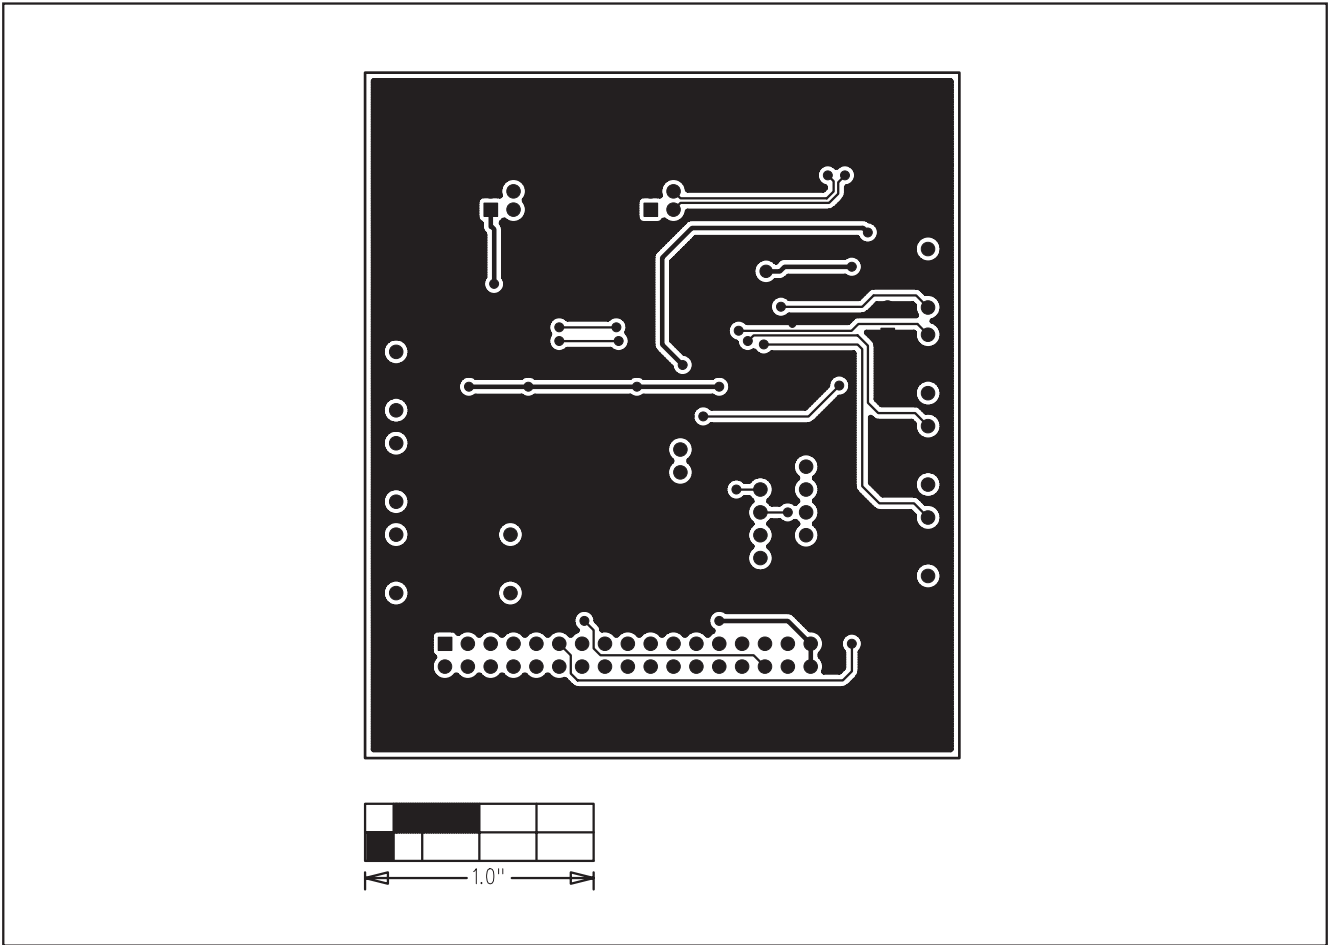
MAX3421评估板-1 PCB布局—焊接层
